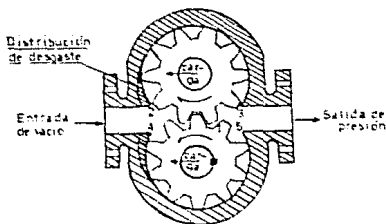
Características básicas de bombeo de la bomba de engranes de baja presión
